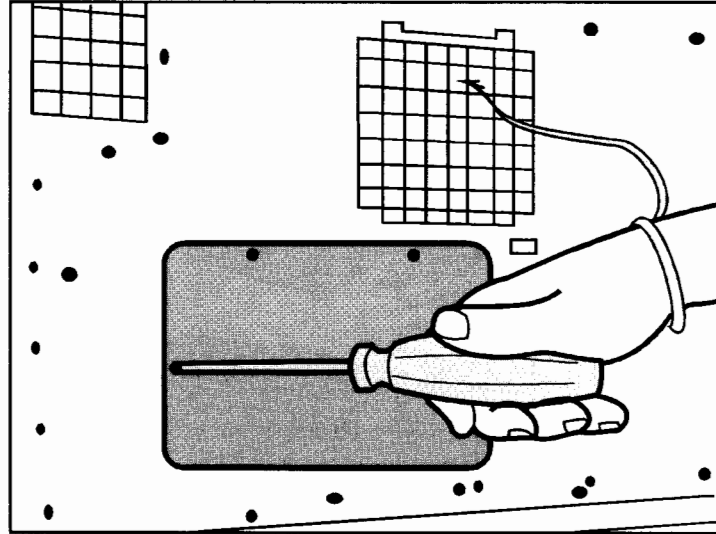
Cómo Retirar la Placa de la Cubierta Metálica
